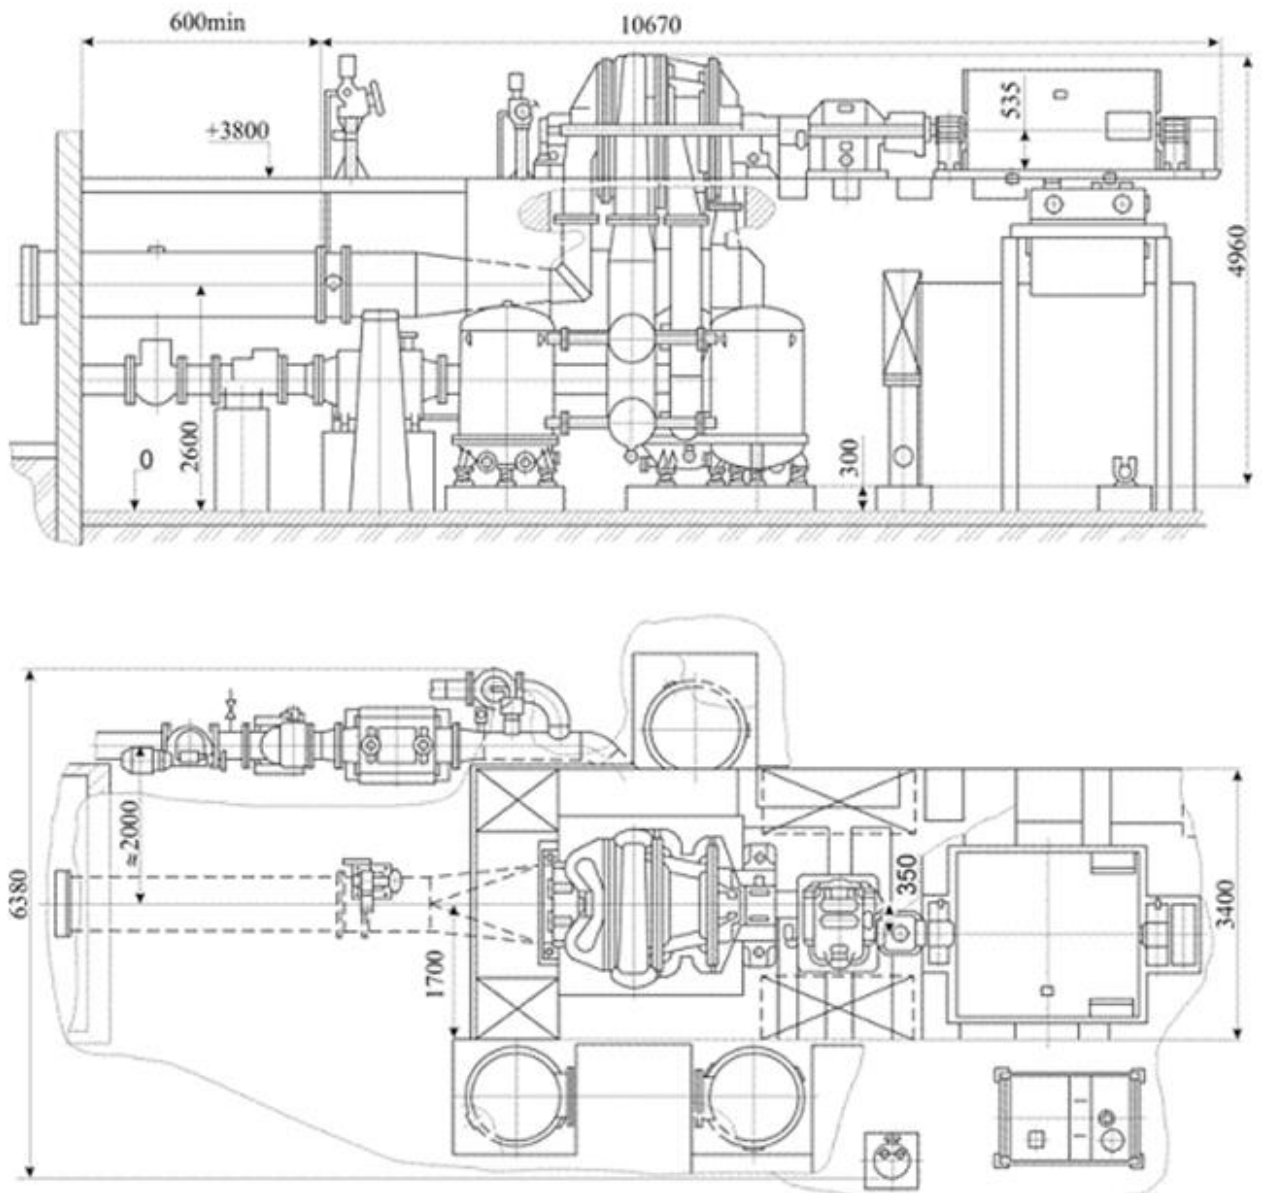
Загальний вид та габаритні розміри компресора К 500-61-5
